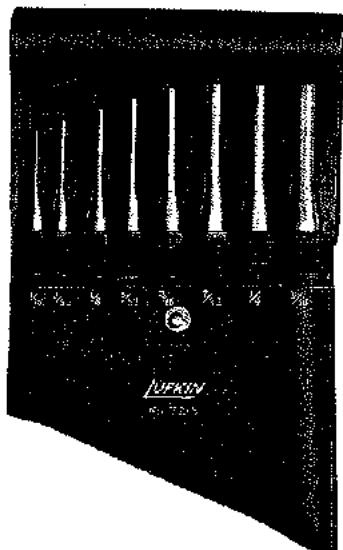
Juego de punteros cilíndricos (Lufkin Rule Co.).
